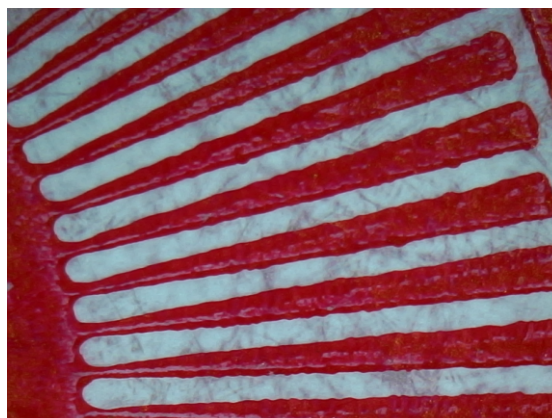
Vzorek L1, CO2 laser, soustředěné paprsky
